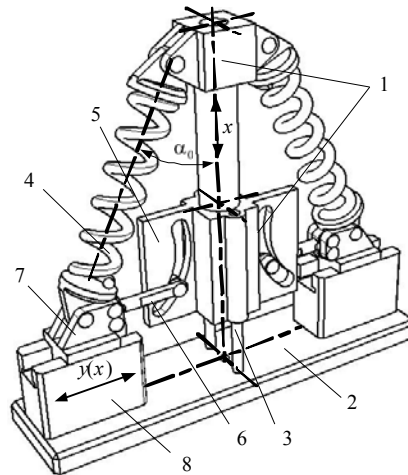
ПДПК з додатковим механічним контуром: 1 – рухома опора; 2 – нерухома опора; 3 – напрямні; 4 – циліндрична пружина; 5 – пластина з направляючим пазом (кулачок); 6 – штовхач; 7 – повзун; 8 – напрямна повзуна
